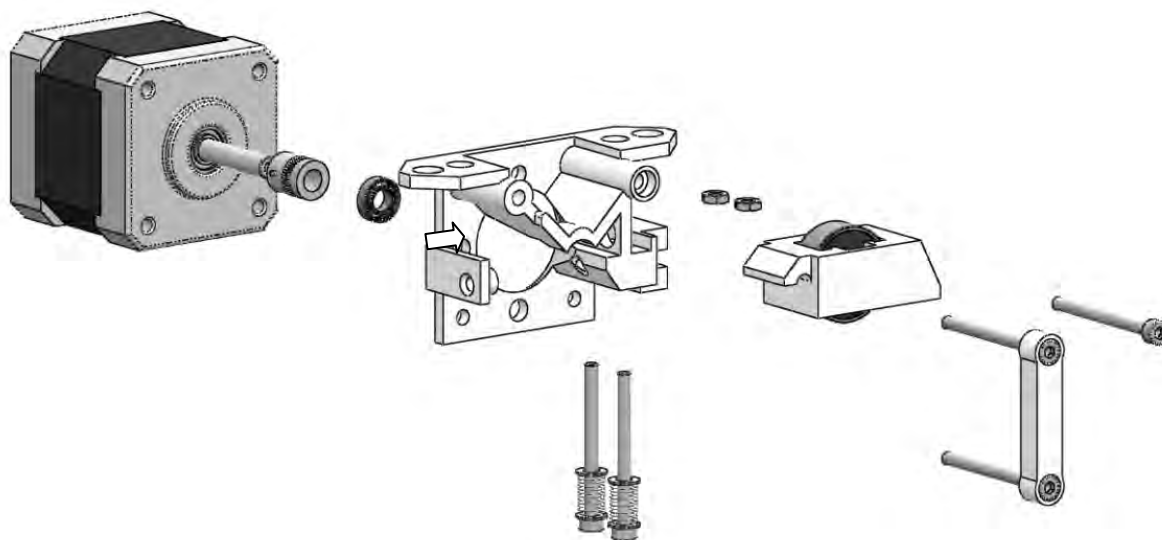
Colocación de engranaje impulsor y mini rodamiento en motor.
